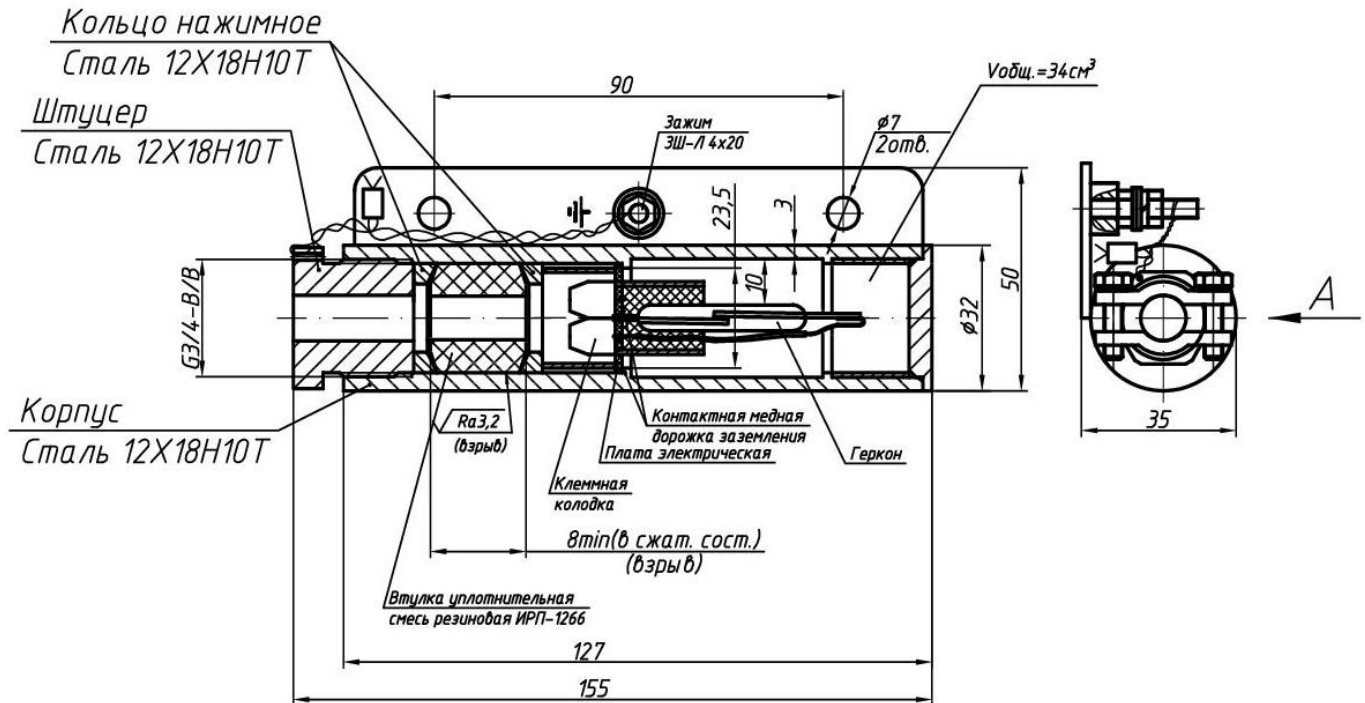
Габаритный чертёж блока датчика извещателей ЕхИО102-1В моделей 01, 02 с элементами взрывозащиты (расположение –левое). Пример маркировки взрывозащиты см в п. 6.1.
